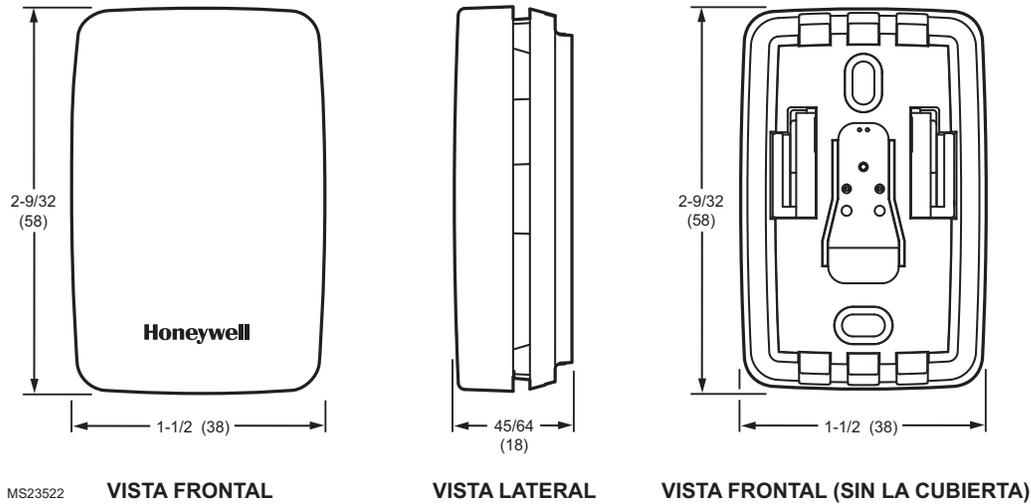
Sensor remoto para interiores C7189U1005. Dimensiones en pulgadas (mm).
